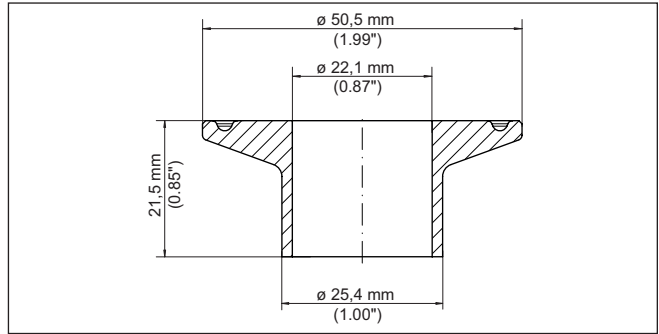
Medidas racor para soldar Clamp 1" (DIN 32676, ISO 2852)
